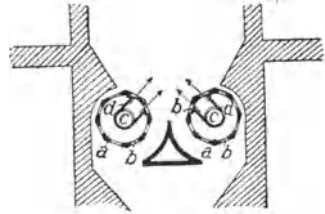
Hohle Brechwalzen mit Druckluftdüsen.
